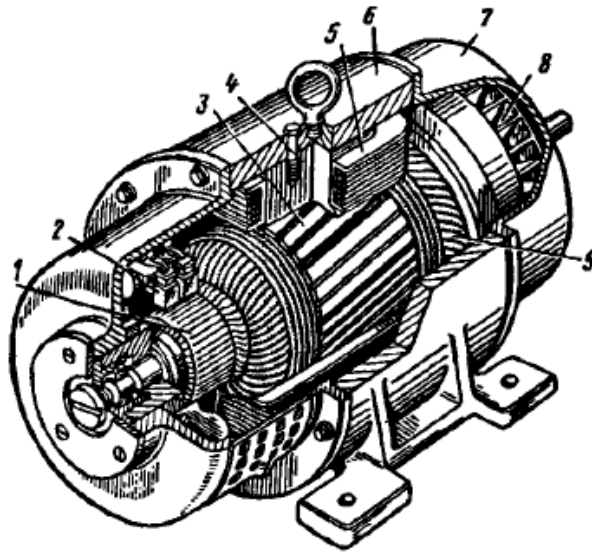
Пристрій машини постійного струму: 1 – колектор; 2 – щітки; 3 – осердя якоря; 4 – осердя головного полюса; 5 – полюсна котушка; 6 – статор; 7 – підшипниковий щит; 8 – вентилятор; 9 – обмотка якоря
